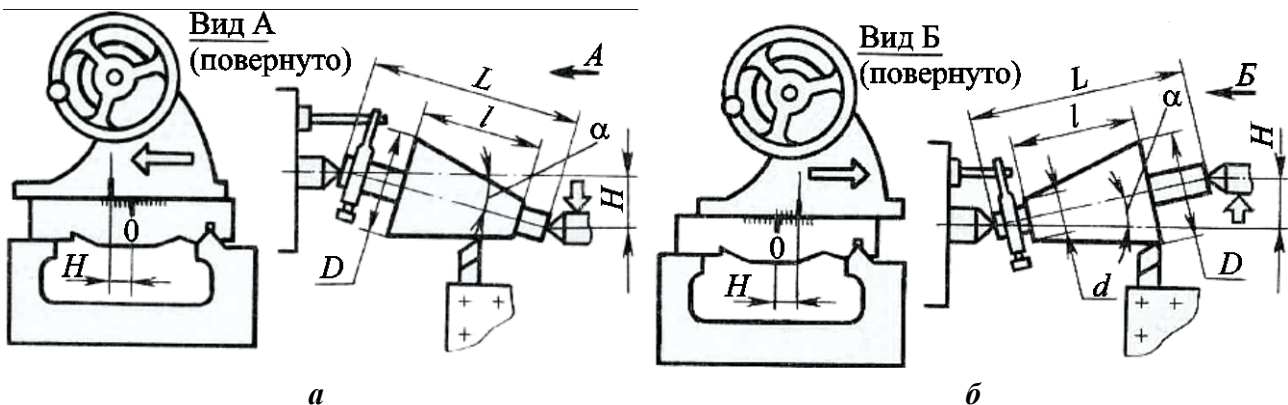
Обробка конічних поверхонь зміщенням корпусу задньої бабки
